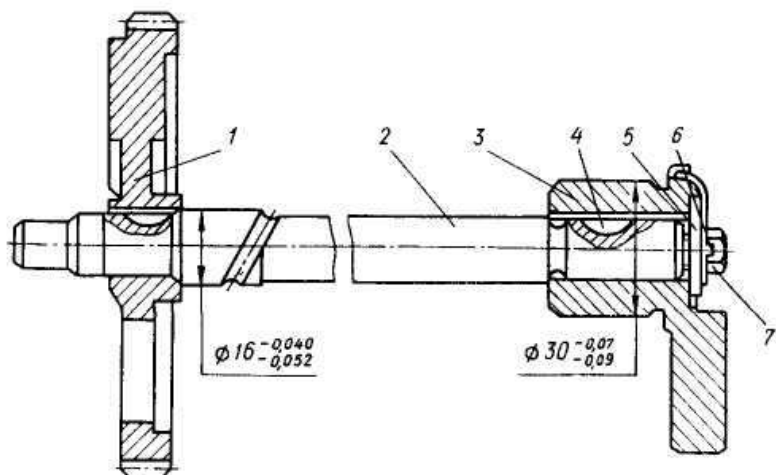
Механизм балансирующий в сборе: 1 — шестерня балансирующего вала; 2 — вал балансирующий; 3 — балансир; 4 — шпонка сегментная; 5 — шайба балансирующего вала; 6 — шайба стопорная; 7 — болт
